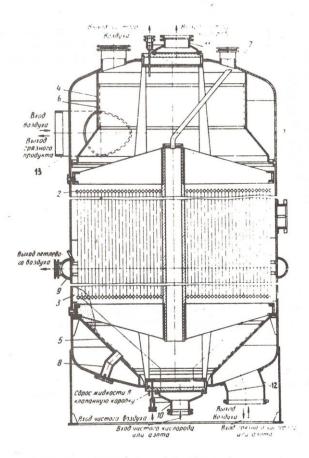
Регенератор с засыпной насадкой и встроеным змеевиком. I-корпус, 2-змеевик; 3-насадка; 4-обечайка; 5-конус; 6-сетка; 7,8,9,10,11, 12,13 - патрубки.
